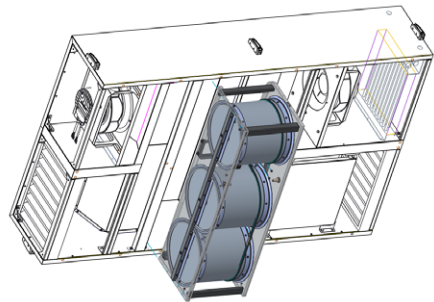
Очистка и разборка оборотного теплообменника RR.
